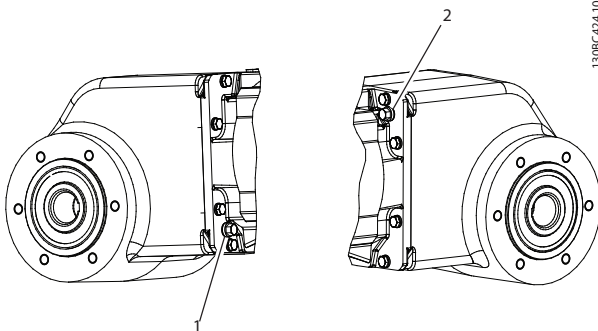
Ölschrauben 1 und 2 des VLT OneGearDrive
